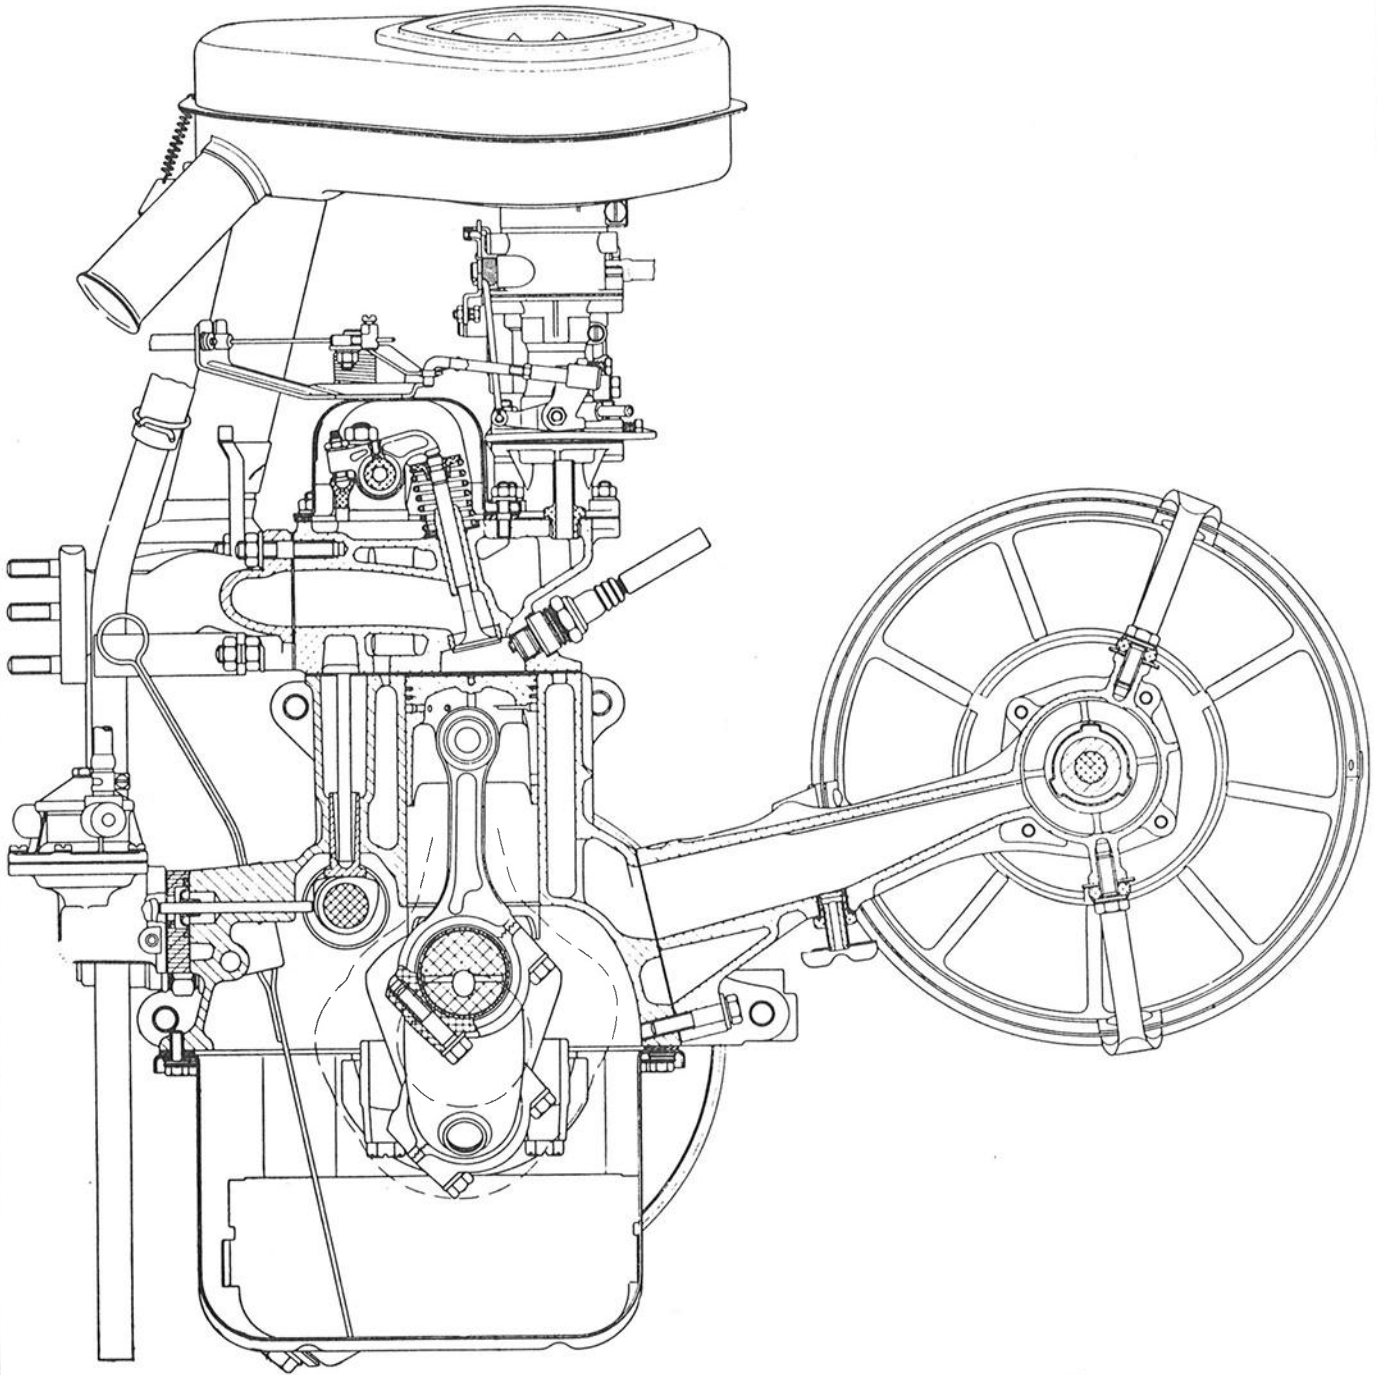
Querschnitt des Motor durch Kurbeltrieb, Steuerung und Kühlwasserpumpe.
